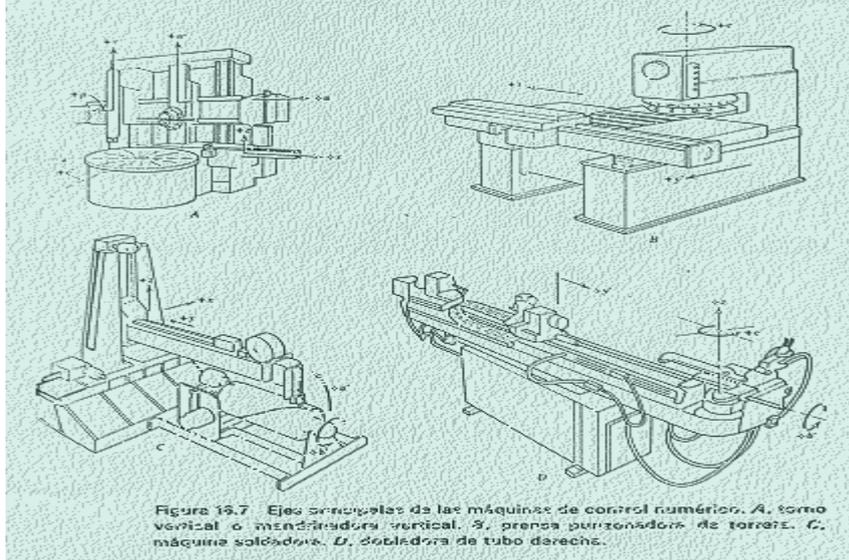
Ejes principales de las máquinas de control numérico. A, torno vertical o mandrinadora vertical. B, prensa perforadora de torre. C, máquina soldadora. D, soldadora de tubo derecho.
